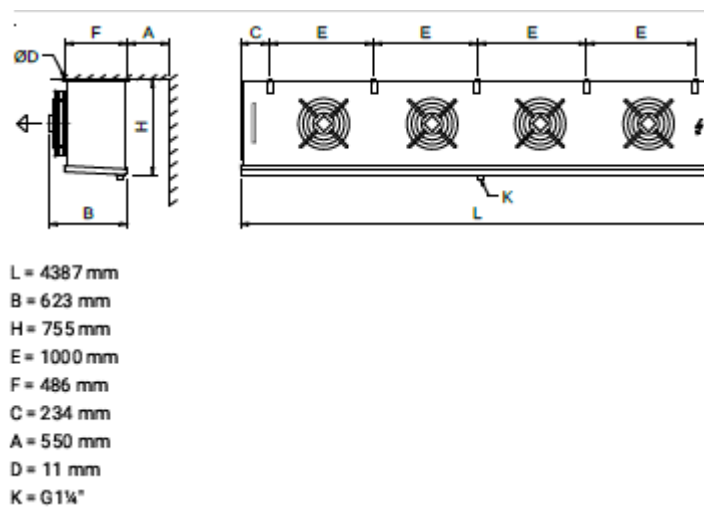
Dimensiones de evaporadores para la Cámara de Maduración.
